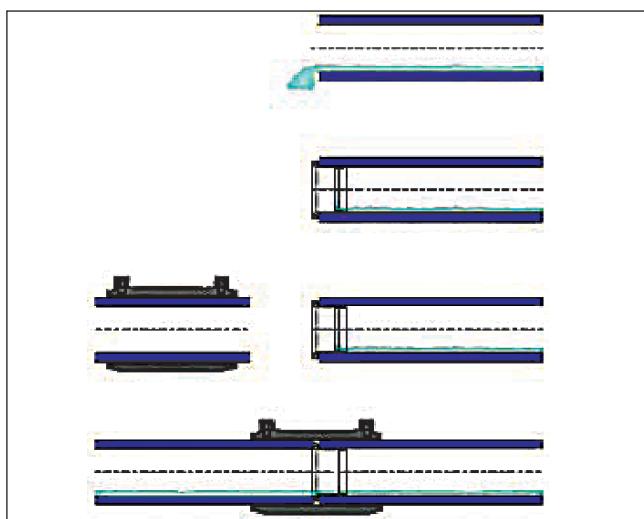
Временное перекрытие зоны сварки при помощи мембраны, растворимой в воде.
